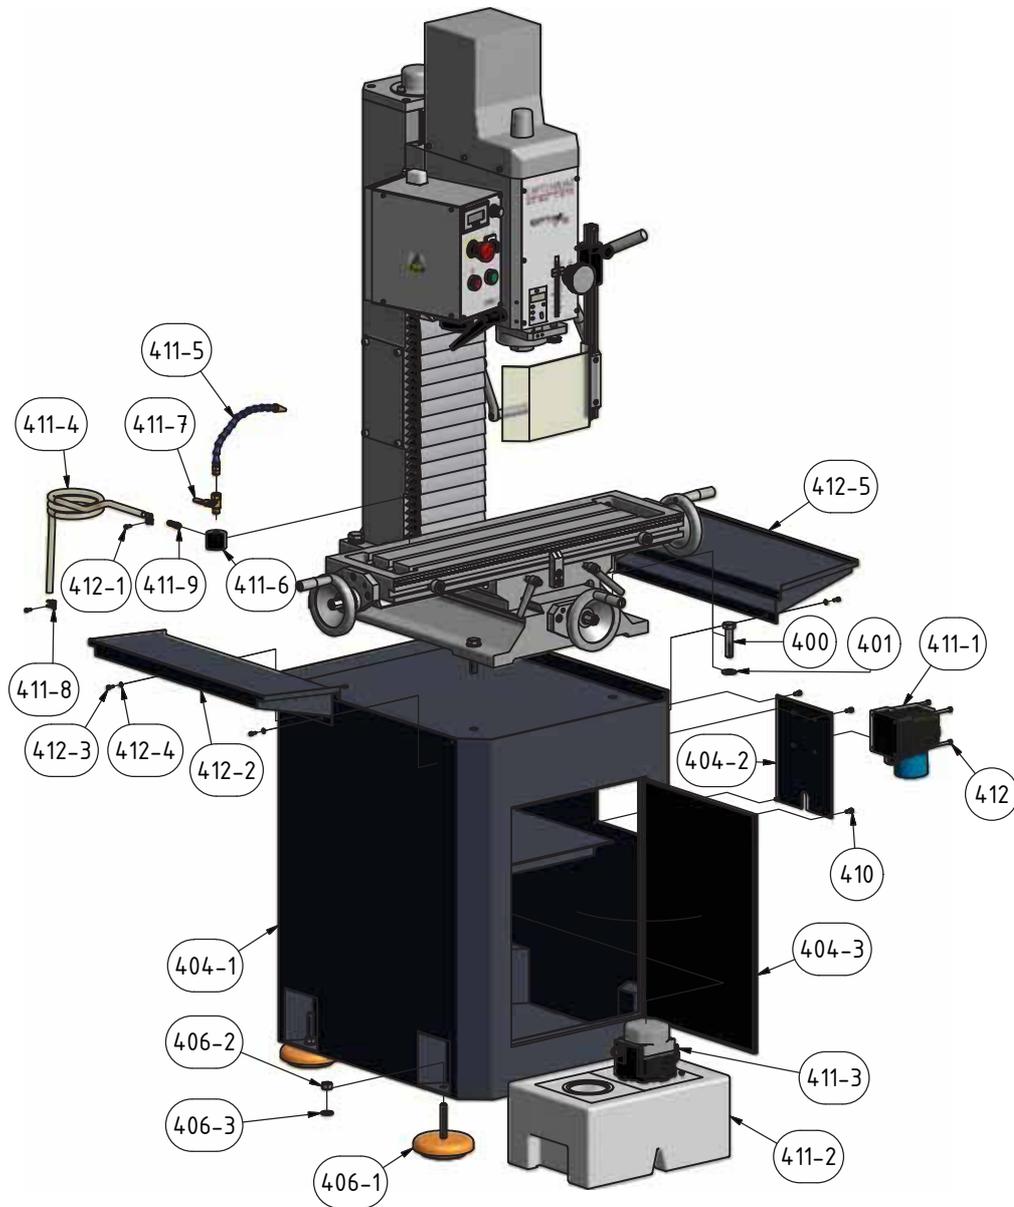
Maschinenunterbau (optional)- Machine stand (option)
